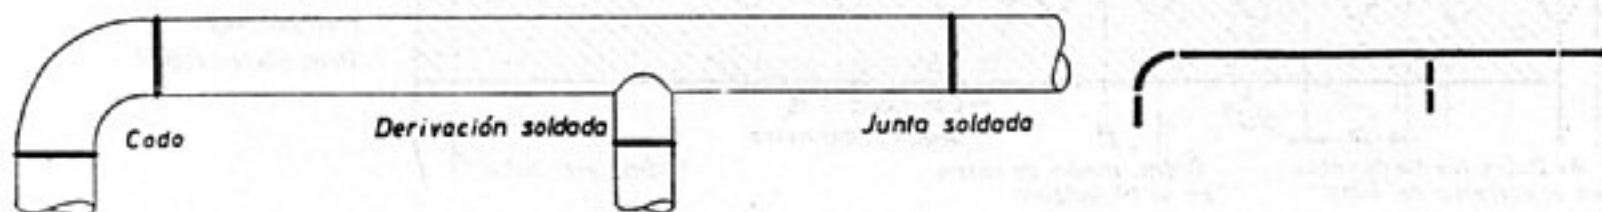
Representaciones de tuberías soldadas.
